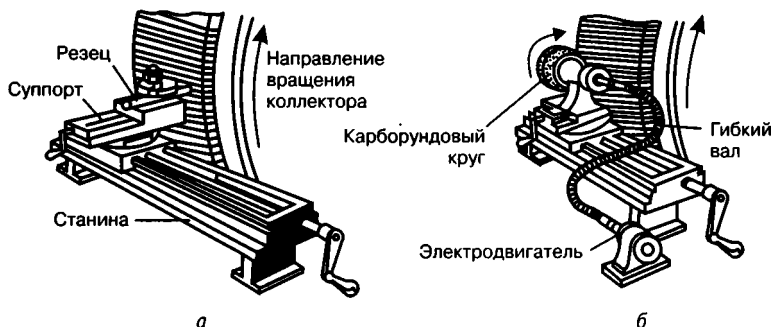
Переносные приспособления для обточки (а) и шлифовки (б) коллектора
